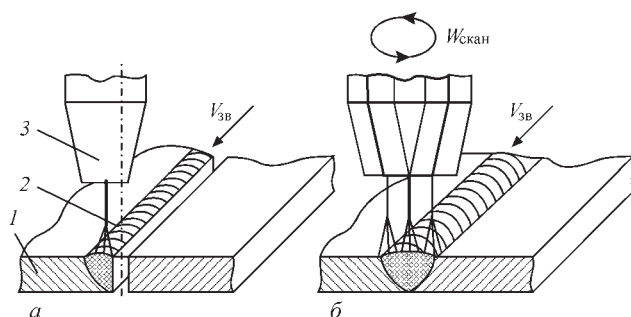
MAG зварювання тонколистового металу: а – зварювання без скануючих рухів пальника (дуга перекинулася на одну із крайок і плавить тільки її в зоні стику); б – зварювання зі скануючими рухами пальника поперек стику або по колу
